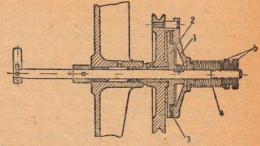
Наматывающее устройство нижней противопожарной коробки: 1 и 2 — фланцы; 3 — шайба; 4 — пружина; 5 — гайки
